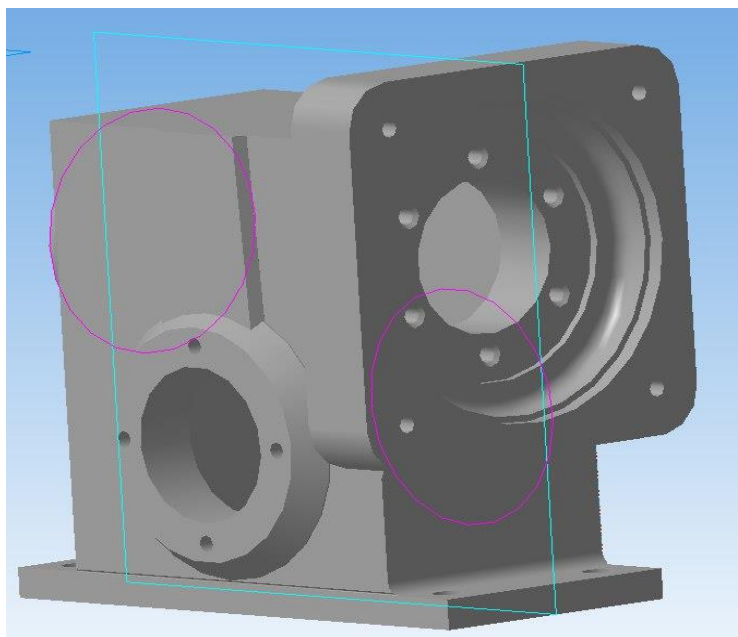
3D модель детали «Корпус редуктора водяной помпы»
